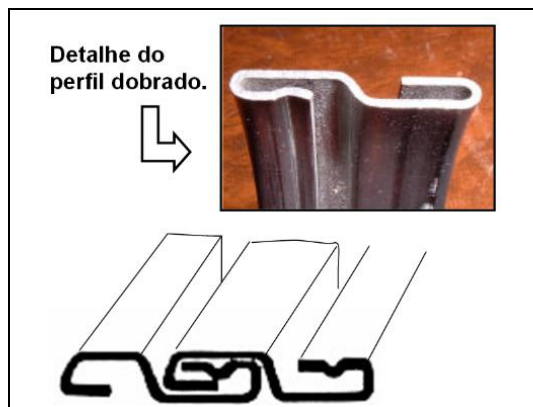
Detalhe da carcaça metálica da armadura de uma linha flexível.
